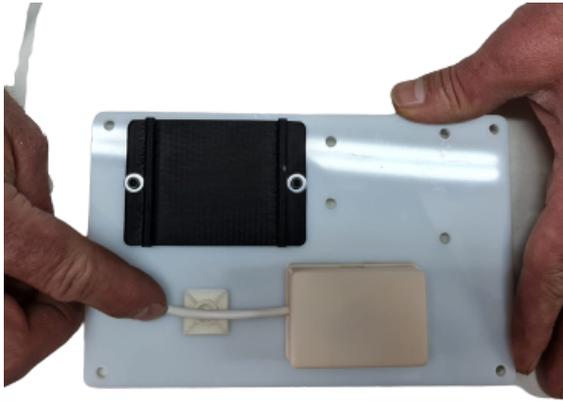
Detalle de la sujeción del cable 1 por medio de una brida y un soporte adhesivo para la misma, situado en el soporte del *kit* electrónico.
